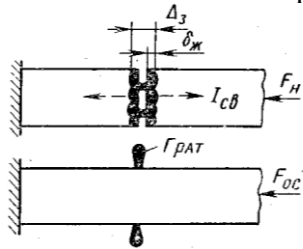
Схема образования соединения при стыковой сварке оплавлением (F_n – начальное усилие; $F_{ос}$ – усилие осадки; Δ_3 - зазор между деталями; $\delta_{ж}$ - слой расплавленного металла).
